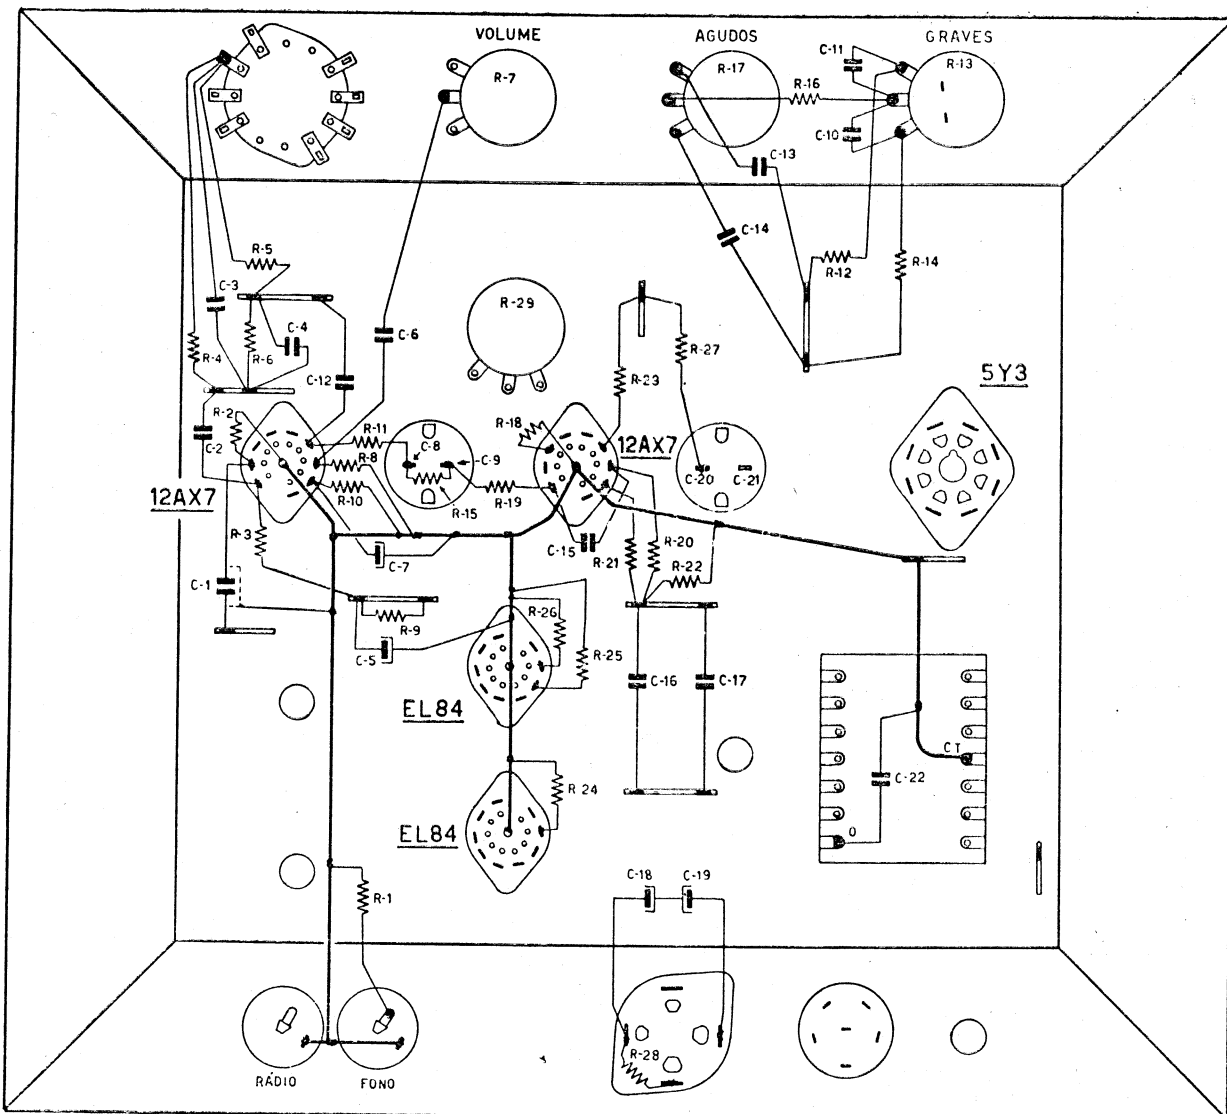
Desenho chapeado dos componentes a serem colocados para completar a montagem.
